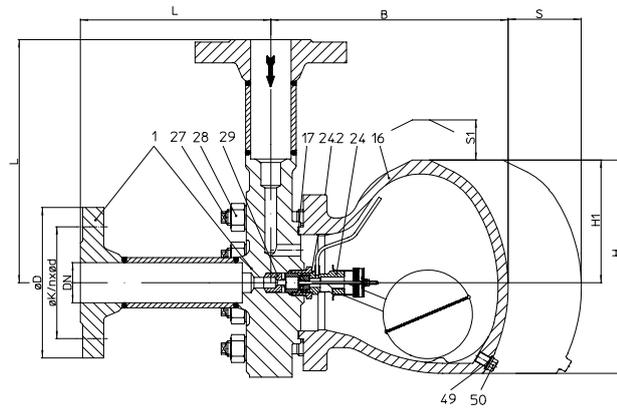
1 ECK-Ausführung mit Flanschen - vertikale Einbaulage
